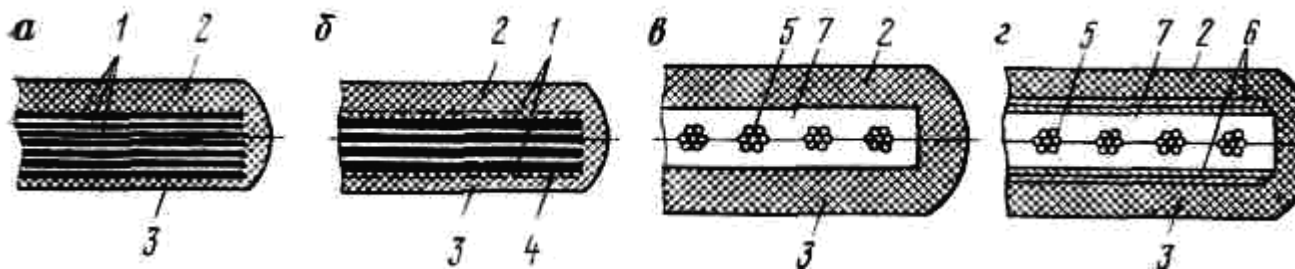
Конструкция конвейерных лент: 1 — прокладки; 2 — верхняя рабочая обкладка; 3 — нижняя обкладка; 4 — брекерная ткань; 5 — трос; 6 — предохранительная прокладка; 7 — резиновый наполнитель
